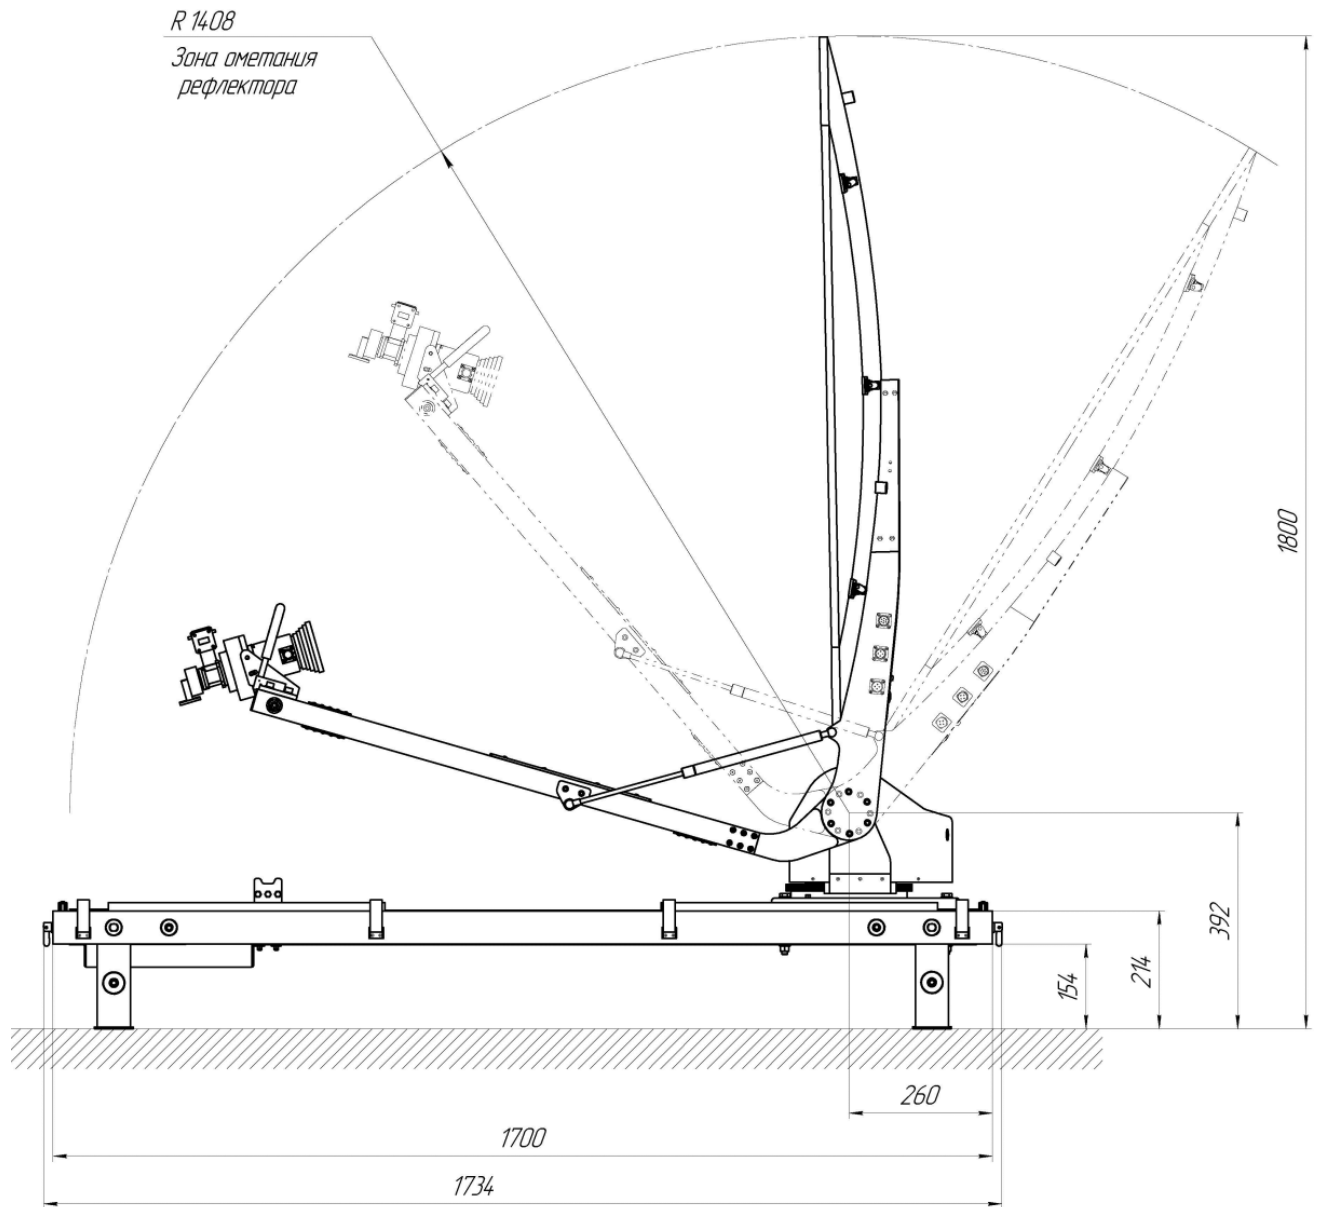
Габаритные размеры и зоны ометания ПК в развернутом состоянии, вид сбоку
